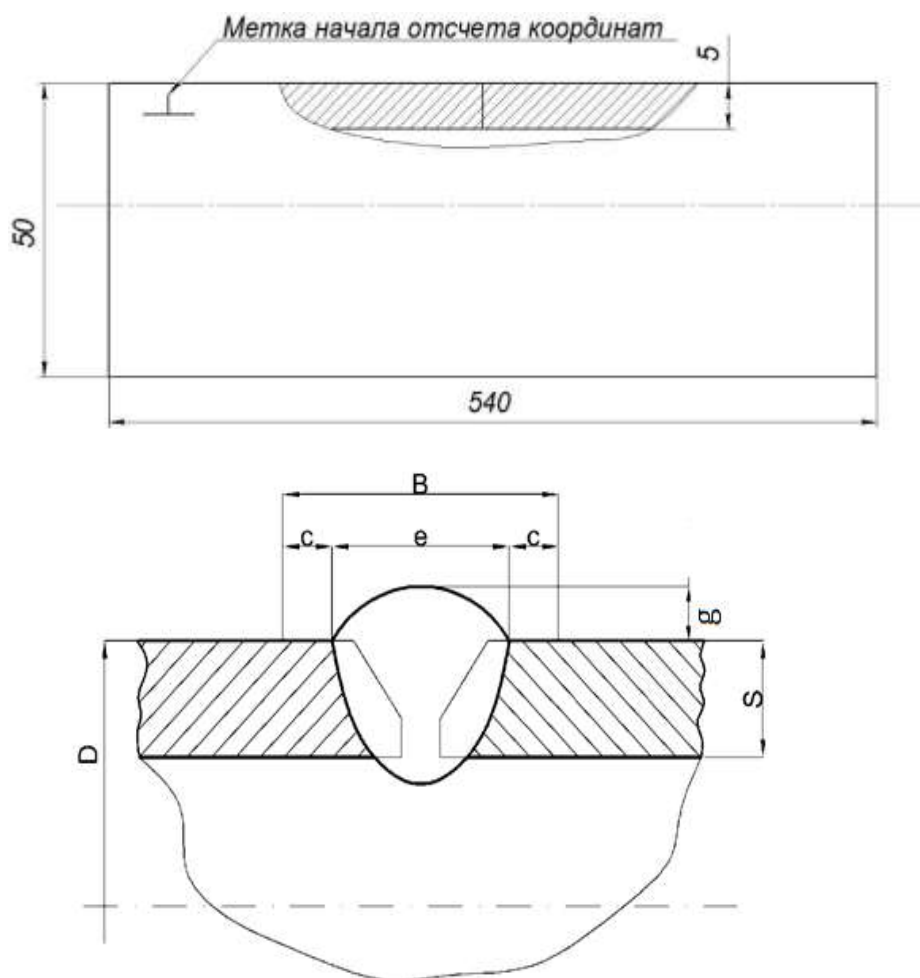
Эскиз образца и сварного соединения
